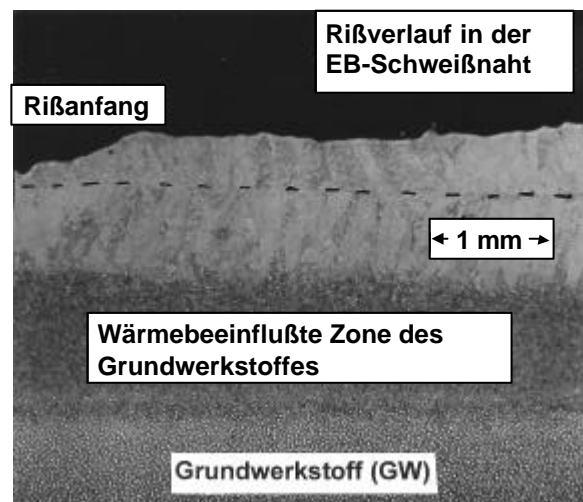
Querschliff durch eine gebrochene LCF-Prüfprobe. Der Riß wurde durch eine Bohrung in der EB-Schweißnaht initiiert.
